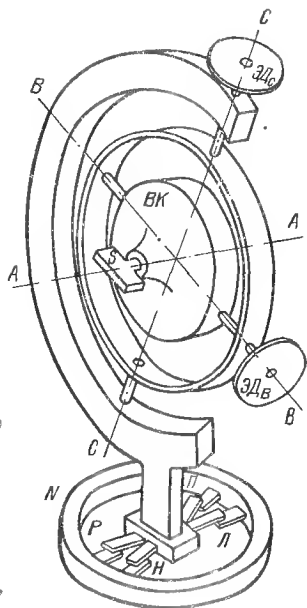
Схема гироскопического приспособления для сварки мелких деталей.
